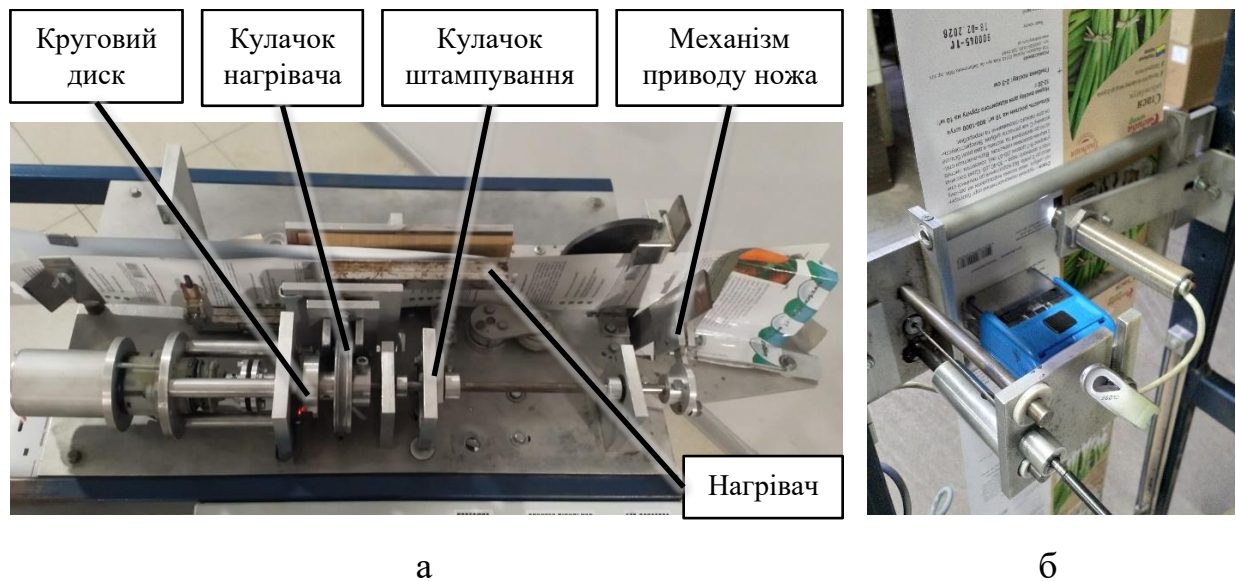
Механізми відрізки, штамповки і запайки пакетів, а – вісь приводящого двигуна, б – печатка, що використовується для позначення дати пакування.
